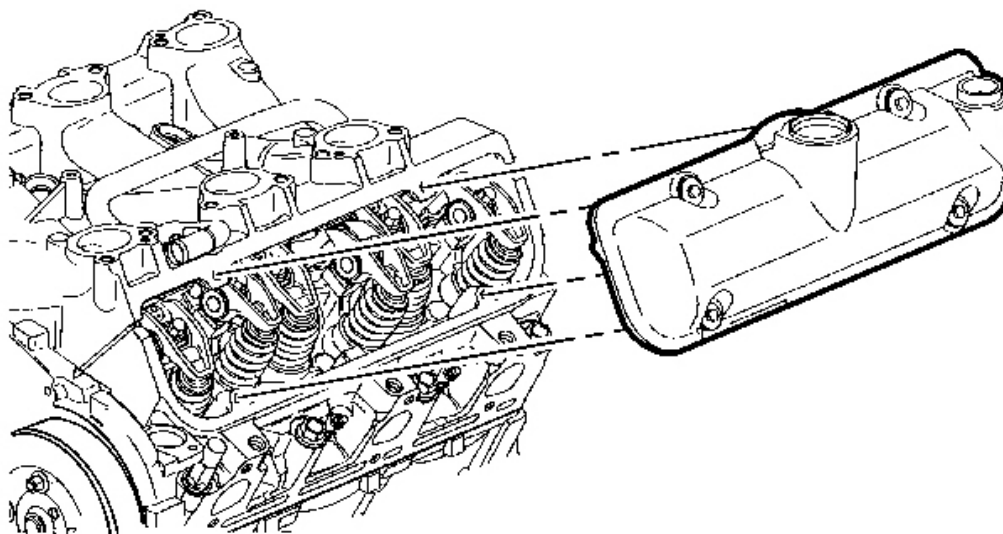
Vista de PCV Baffle, tornillos, PCV Valve & cubierta de la válvula
